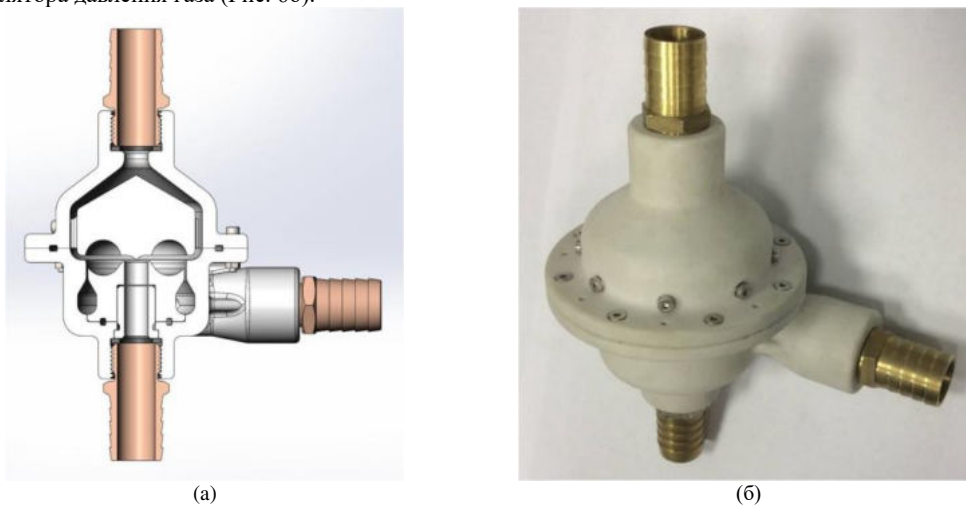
(а) трехмерная модель вихревого регулятора давления газа; (б) экспериментальный образец
